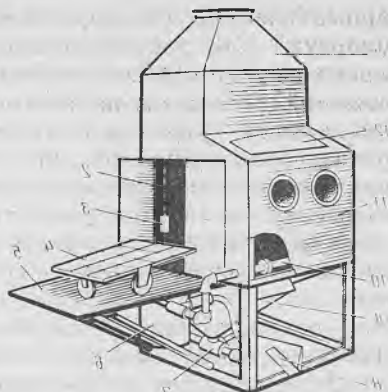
Установка для очистки деталей косточковой крошкой
